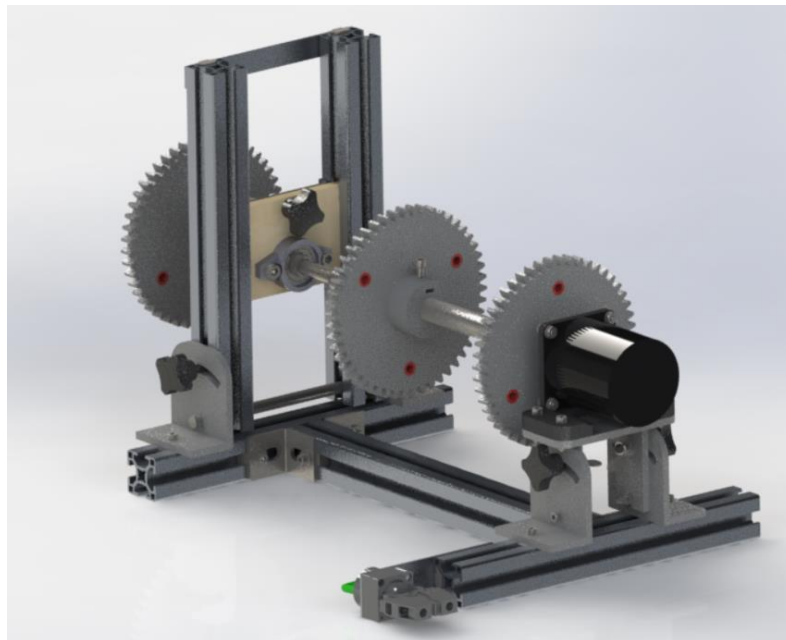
Diseño final del prototipo de doble junta universal cardan.
